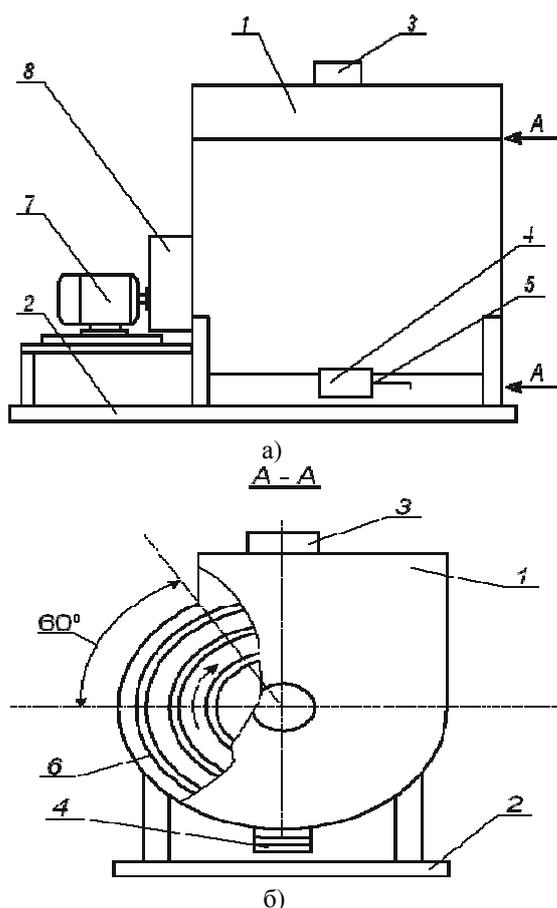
Усовершенствованный горизонтальный ленточный смеситель: а - общий вид; б - вид справа: 1 - чашеобразный бункер; 2 - рама; 3 - загрузочный патрубок; 4 - выгрузной патрубок; 5 - заслонка; 6 - комбинированный шнек; 7 - двигатель; 8 - редуктор
